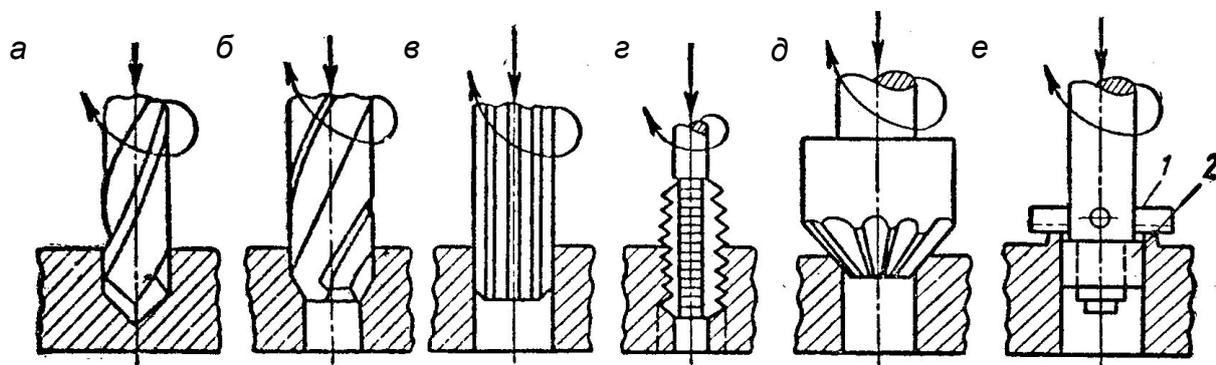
Основные виды обработки на сверлильных станках: *а* – сверление; *б* – зенкерование; *в* – развертывание; *г* – нарезание резьбы; *д* – зенкование; *е* – цекование; 1 – переставной резец; 2 – направляющая часть
